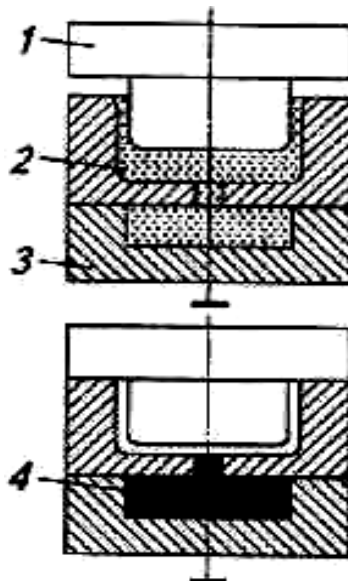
Схема литьевого прессования деталей из пластмасс: 1 - пуансон; 2 - загрузочная камера; 3 - матрица; 4 - деталь
